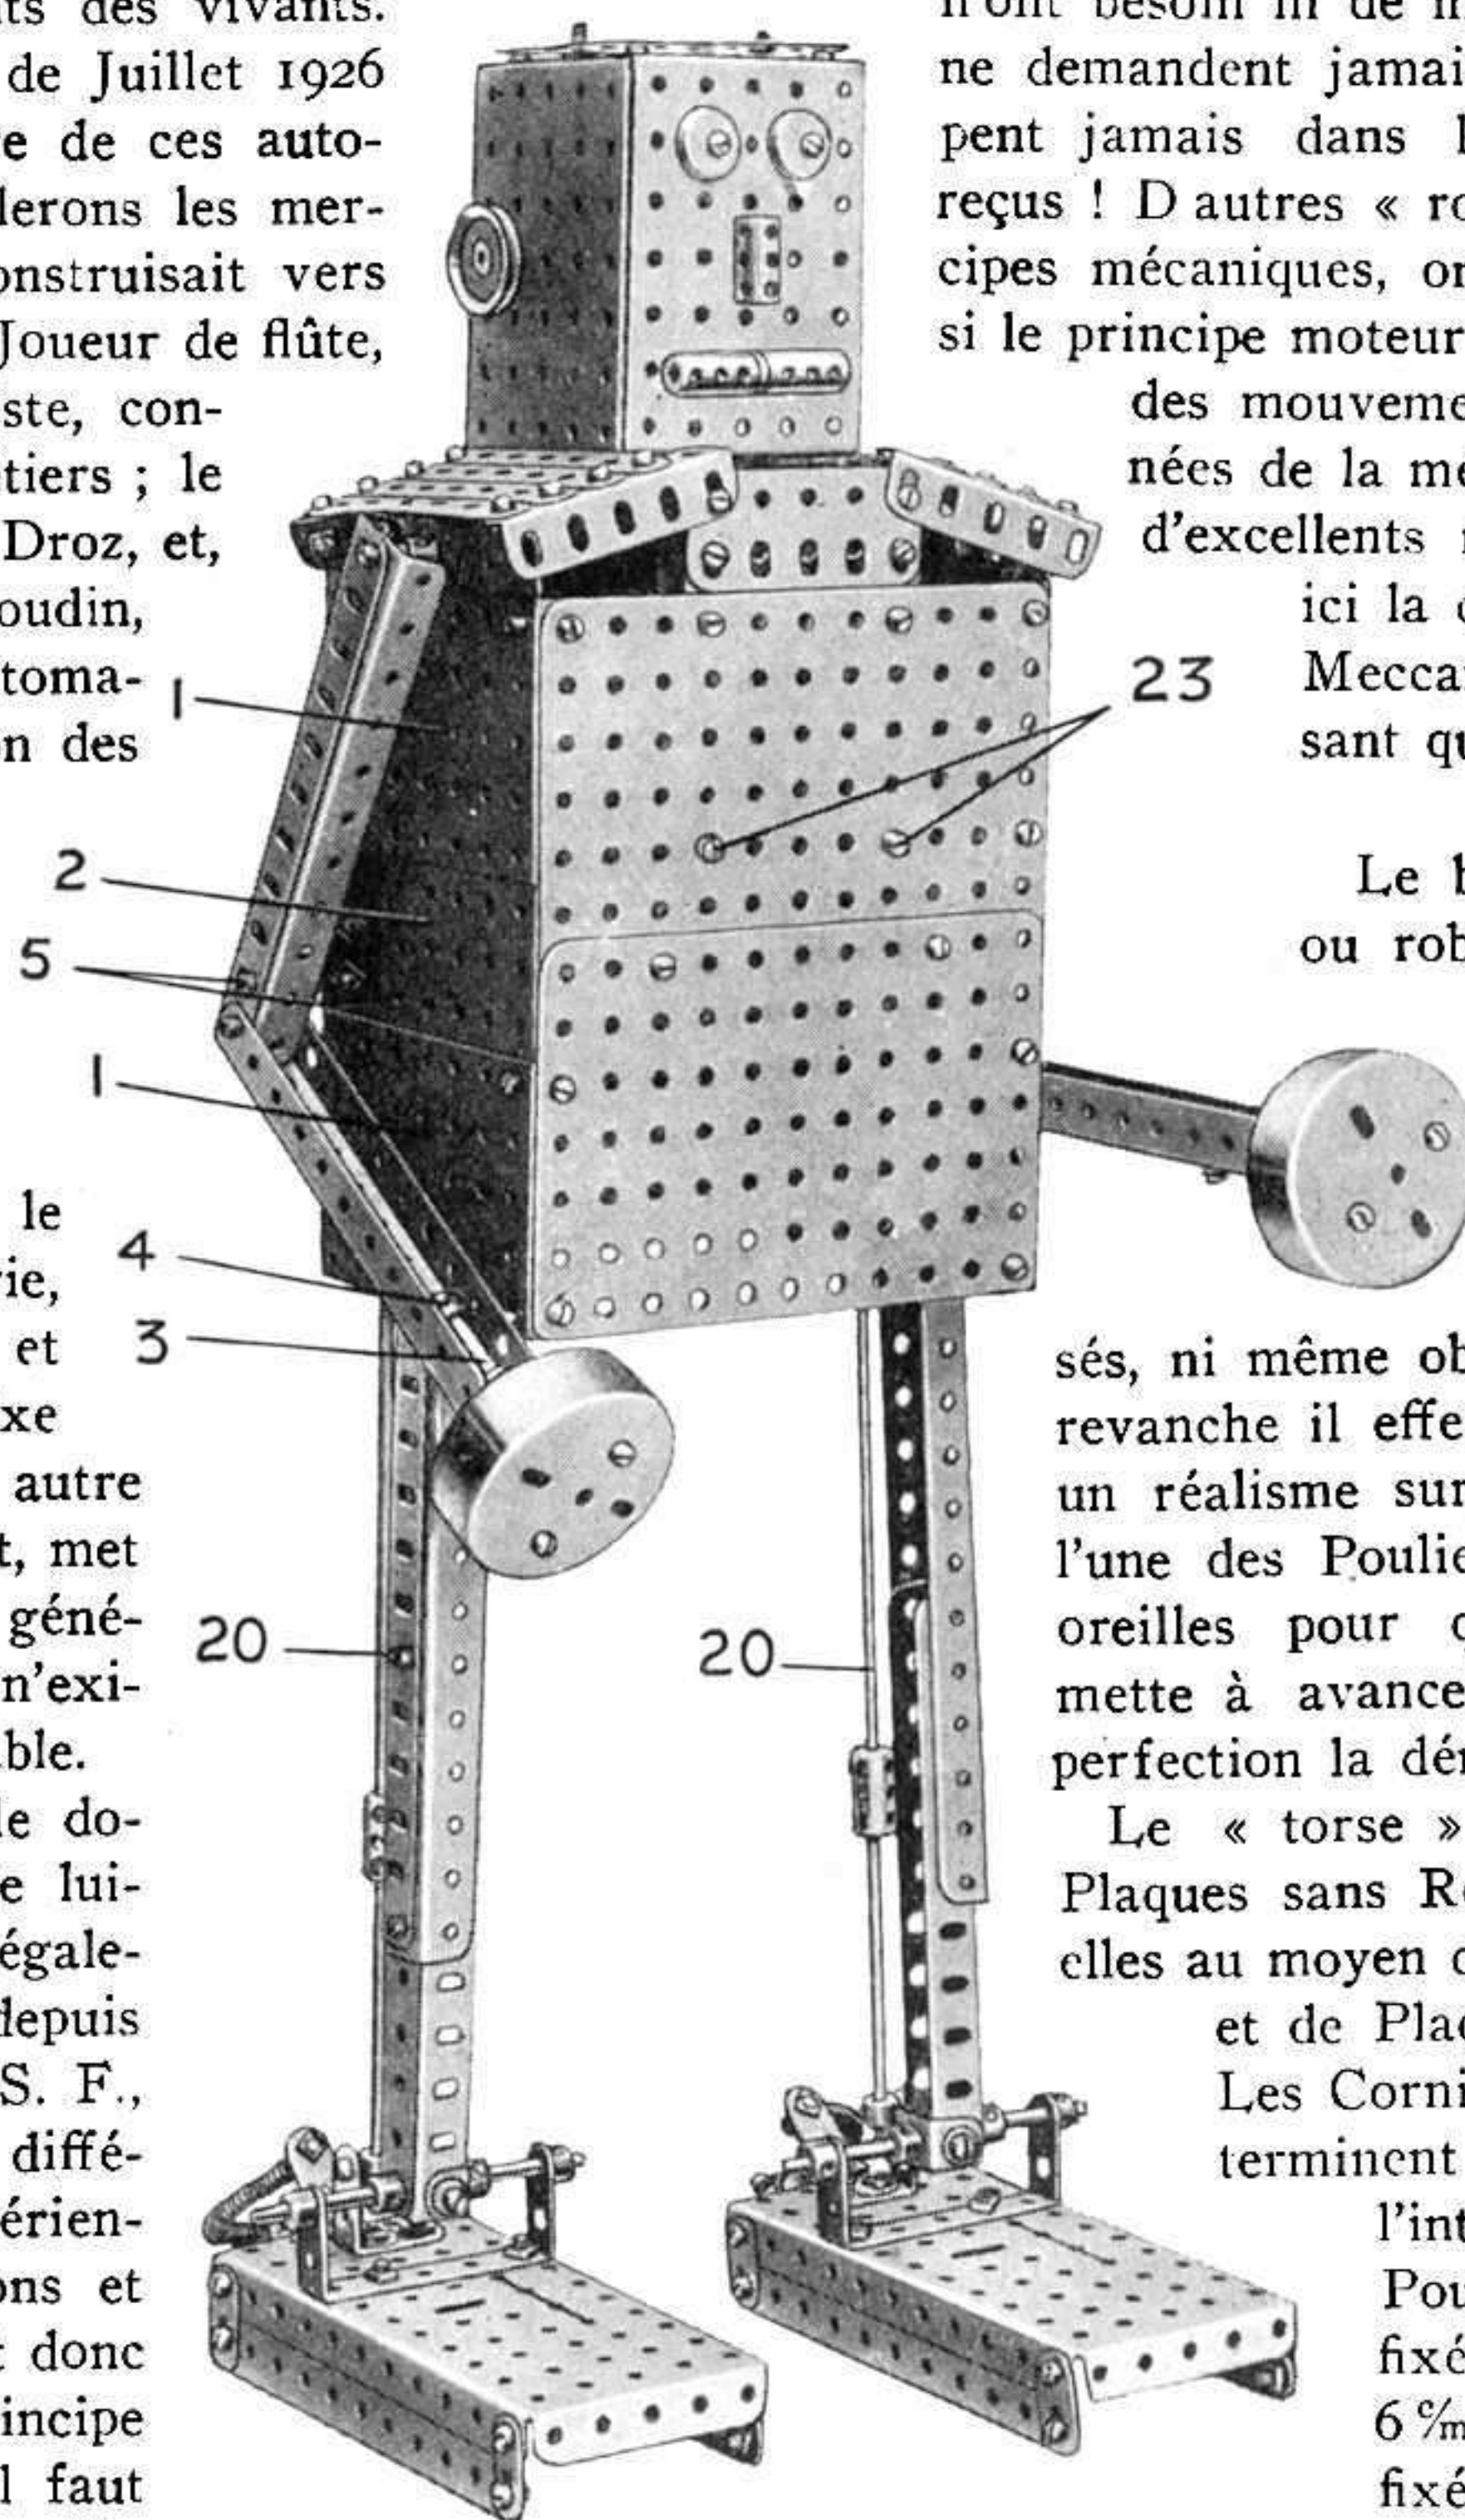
Vue générale du modèle de «Robot» Meccano.
